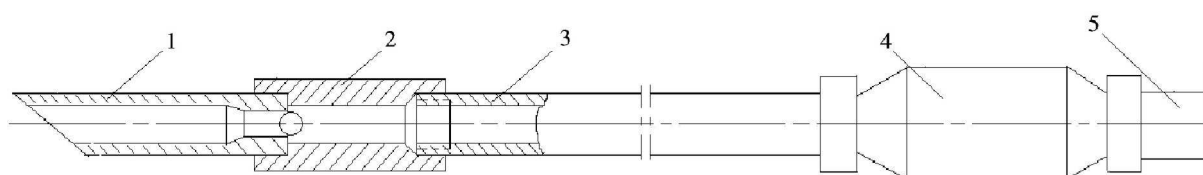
Схема компоновки подземного оборудования при проведении водоизоляционных работ:
